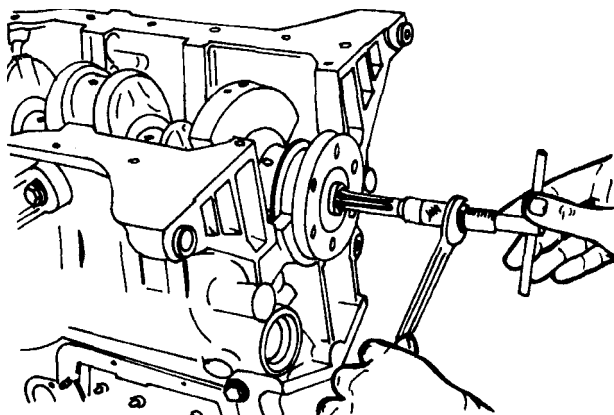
Выпрессовка подшипника первичного вала КПП из коленвала специальным съемником 21-037А.
